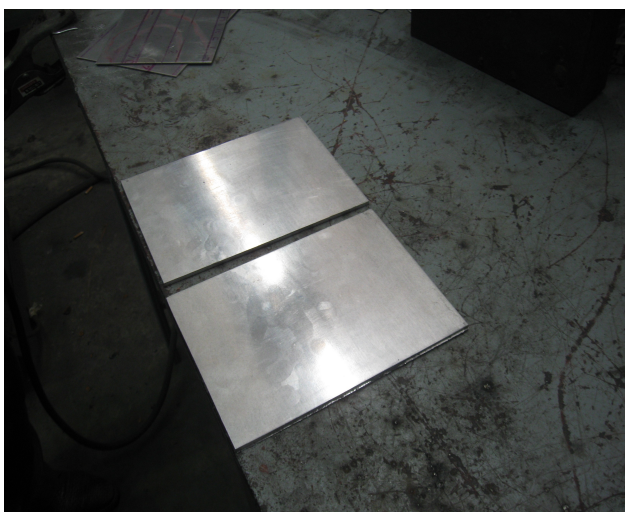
Tôles d'alliage d'aluminium 7075 T6 avant soudage
